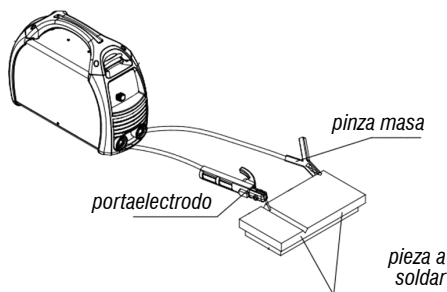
Montaje de los cables de soldadura para soldar Electrodo Recubiertos (MMA)
